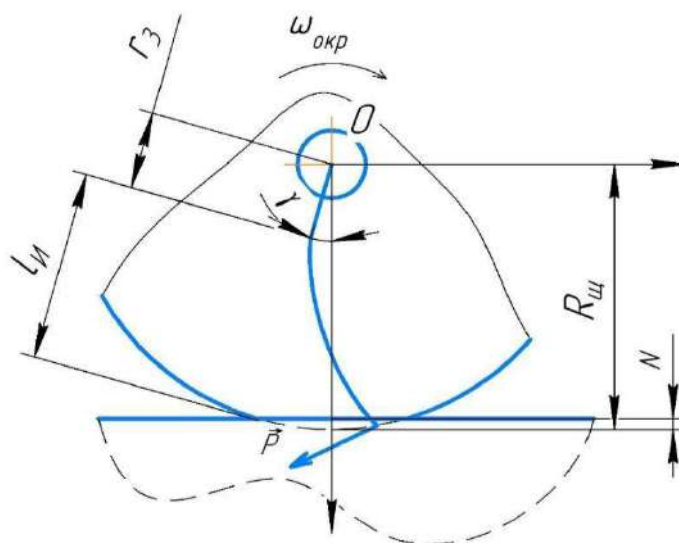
Контакт щітки з плоскою поверхнею зуба рульової рейки
